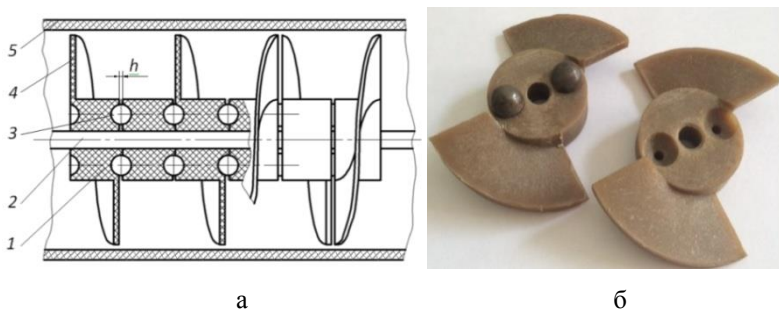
Крильчато-тросовий робочий орган гвинтового конвеєра:
